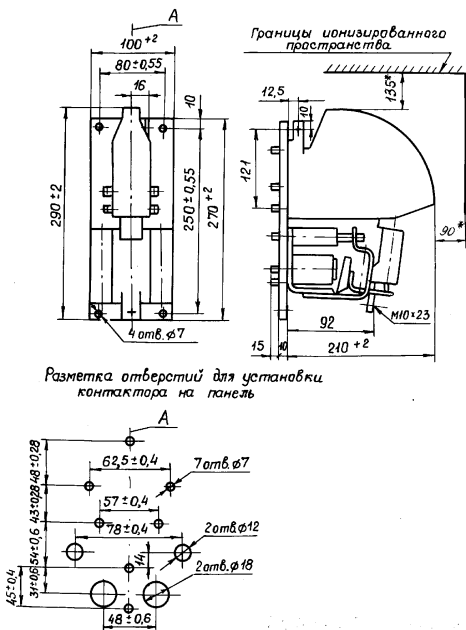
Габаритные, установочные и присоединительные размеры контакторов типа KM24-35. Масса - 6,0 кг
